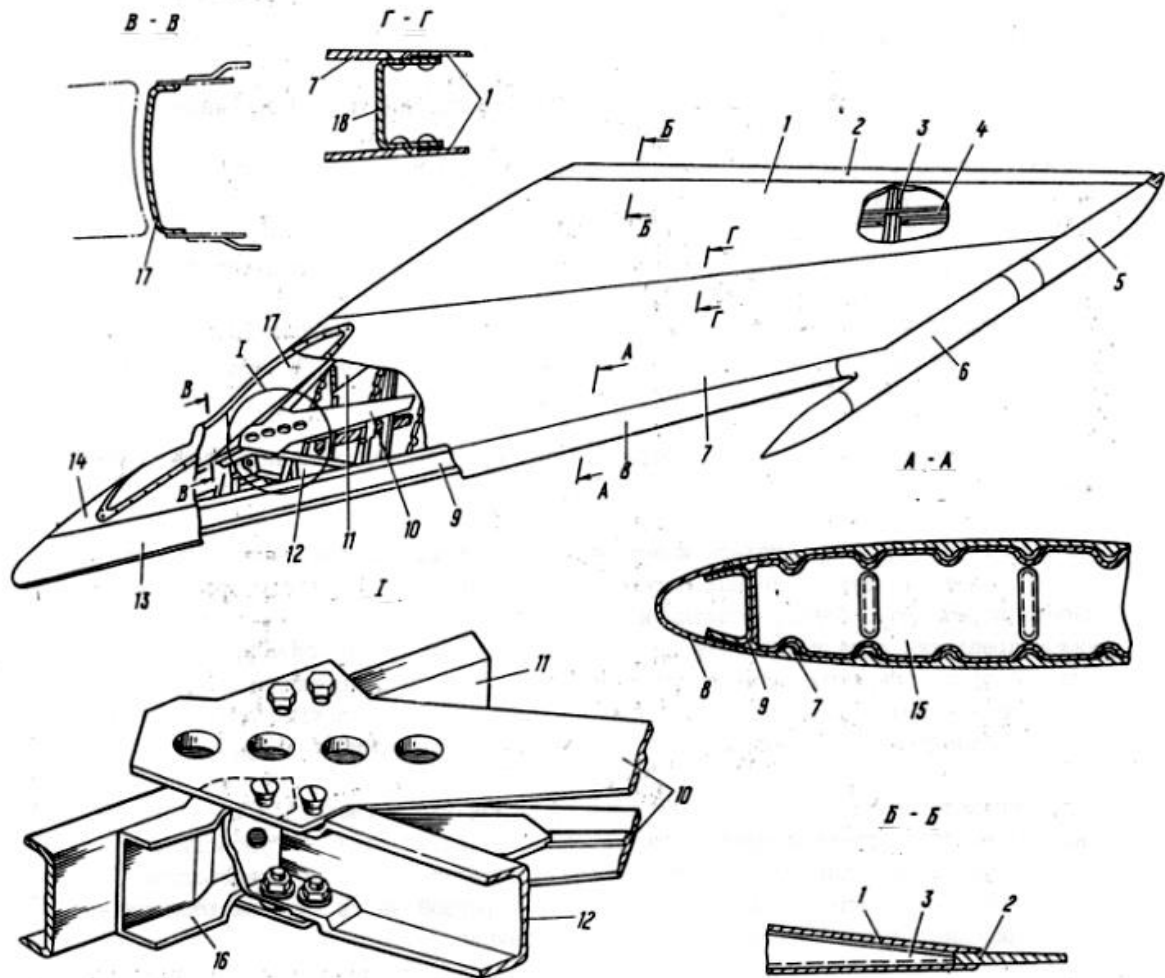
Стабілізатор: 1 – обшивка; 2 – вкладиш кінцевий; 3 - нервюра; 4 – стрингер; 5 – закінцівка; 6 – вантаж протифлатерний; 7 – обшивка; 8 – обшивка носка; 9 – стрингер передній; 10 – накладка; 11 – балка; 12 - подкос; 13 – обшивка носка; 14 – обшивка крила; 15 – нервюра; 16 – коробочка; 17 - нервюра торцева; 18 – стрингер задній
